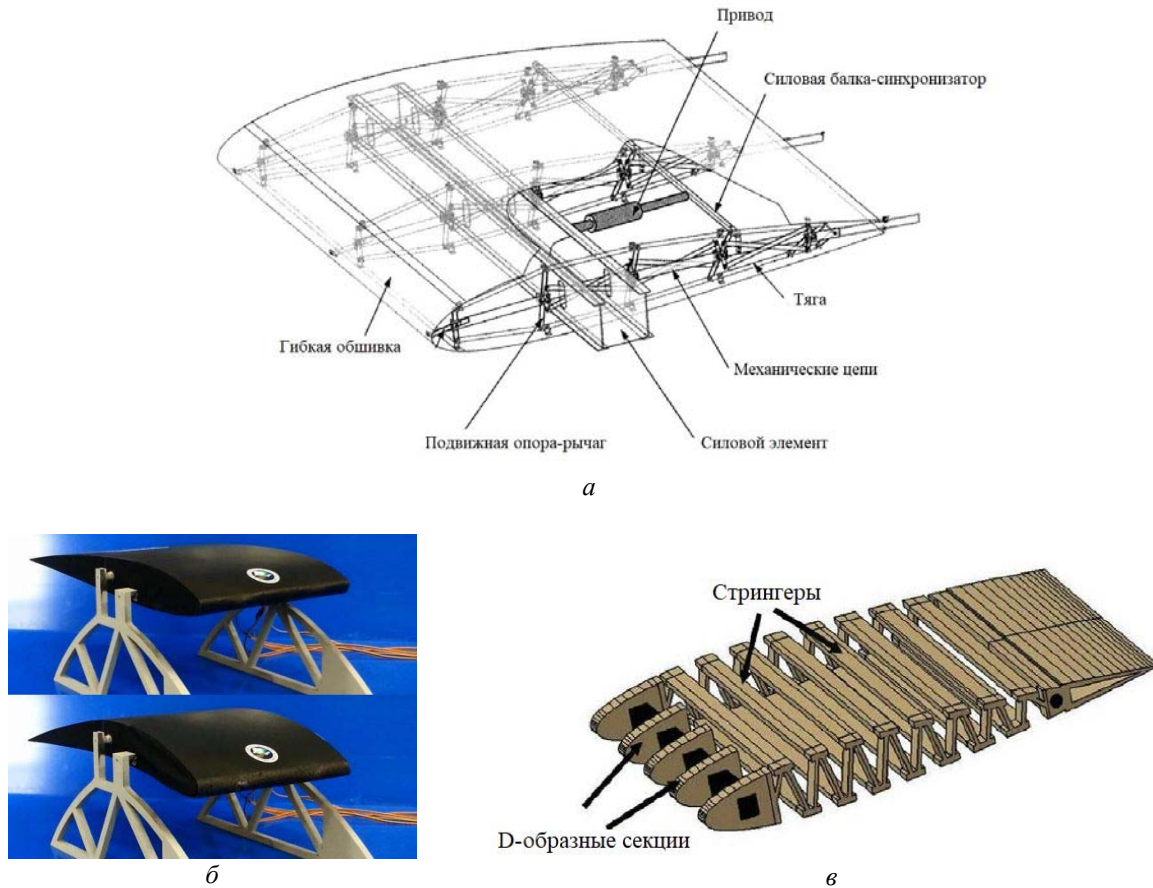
Конструкции крыльев с изменяемой геометрической формой:
